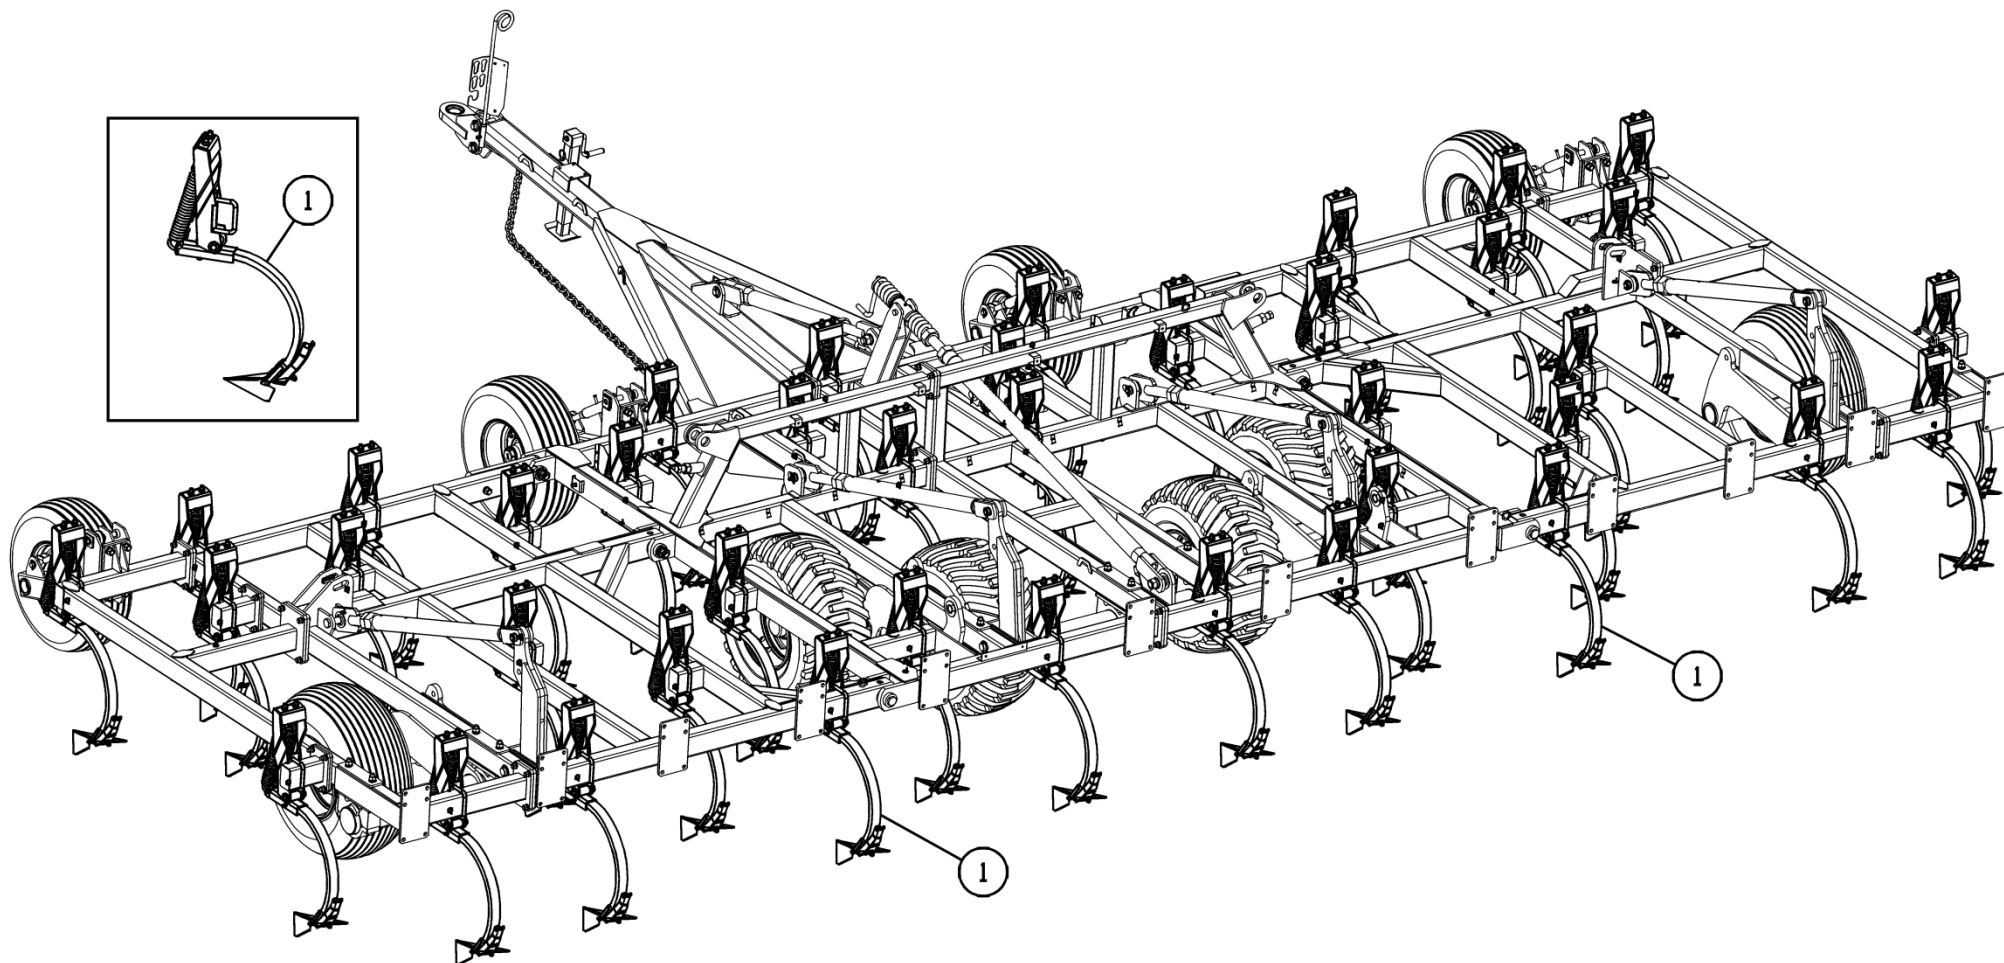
Установка рабочих органов СГ-102.03.000
